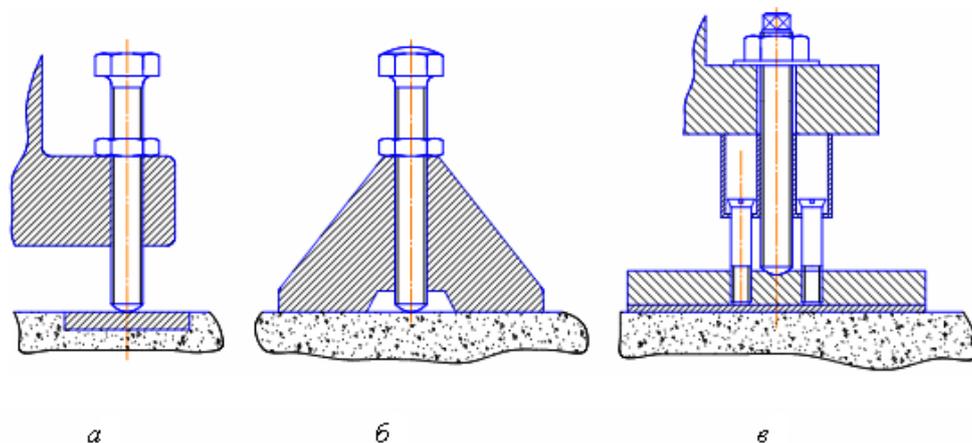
Конструкции винтовых опор для установки станков, незакрепленных болтами
